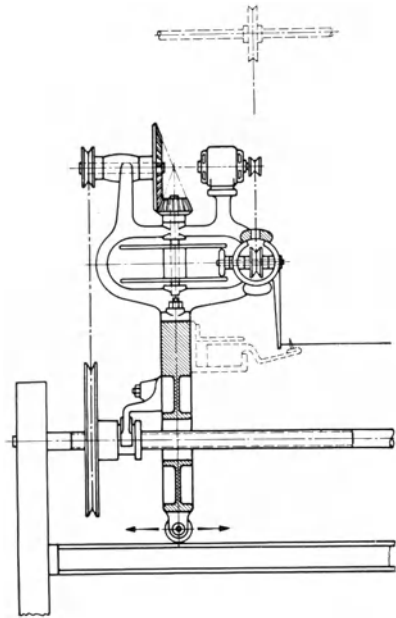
Mechanische Gewebeführungsvorrichtung für Spannrahmen-Trockenmaschinen.
